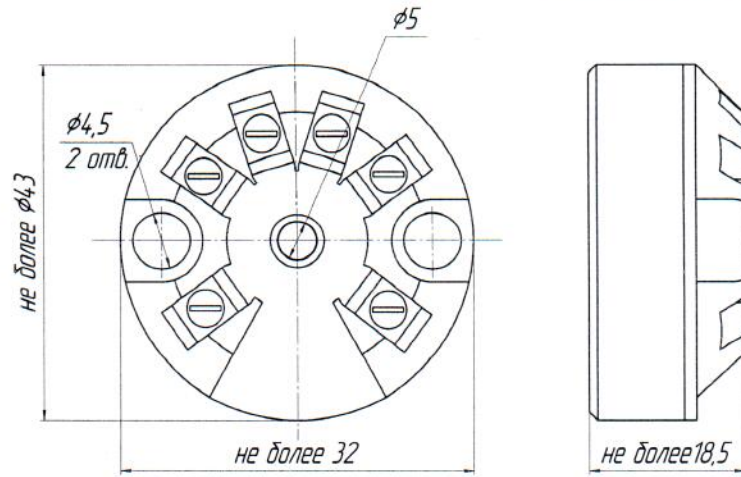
Преобразователь, с конструктивным исполнением К с цифровым протоколом или без цифрового протокола, для крепления в клеммной голове ПП. Степень защиты оболочки IP20.
